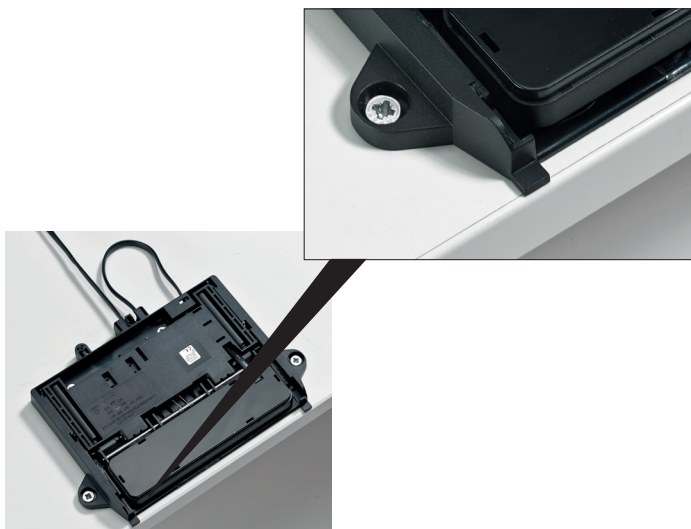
Montageposition des Handschalters LegaDrive Touch Comfort
